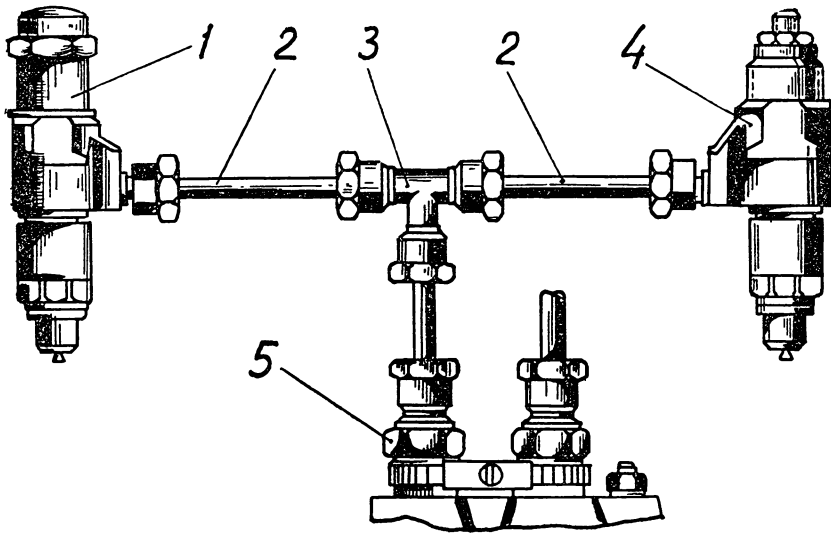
Проверка давления начала впрыска топлива при помощи эталонной форсунки:
